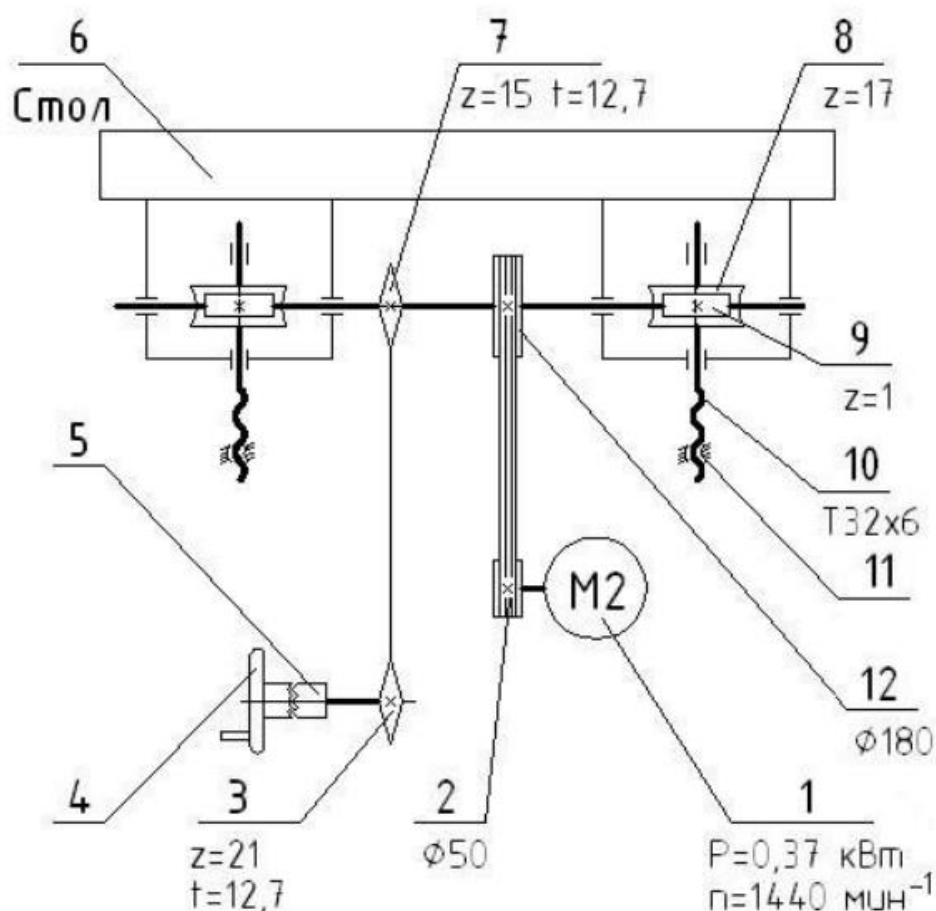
Механизм подъема стола рейсмусового станка SUPERMAC 163
